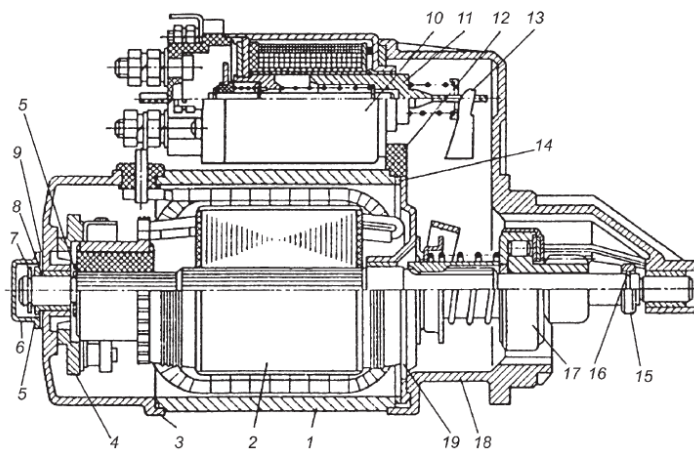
Стартер 421.3708: 1 – корпус; 2 – якорь; 3, 18 – крышки со стороны коллектора и привода; 4 – траверса; 5 – регулировочная шайба; 6 – колпак; 7, 8 – стопорная и упорная шайбы; 9 – прокладка; 10 – тяговое реле; 11 – якорь реле с возвратной пружиной; 12 – заглушка; 13 – рычаг включения привода; 14, 15, 16 – уплотнительное, упорное и замковое кольца; 17 – механизм привода; 19 – промежуточная опора
